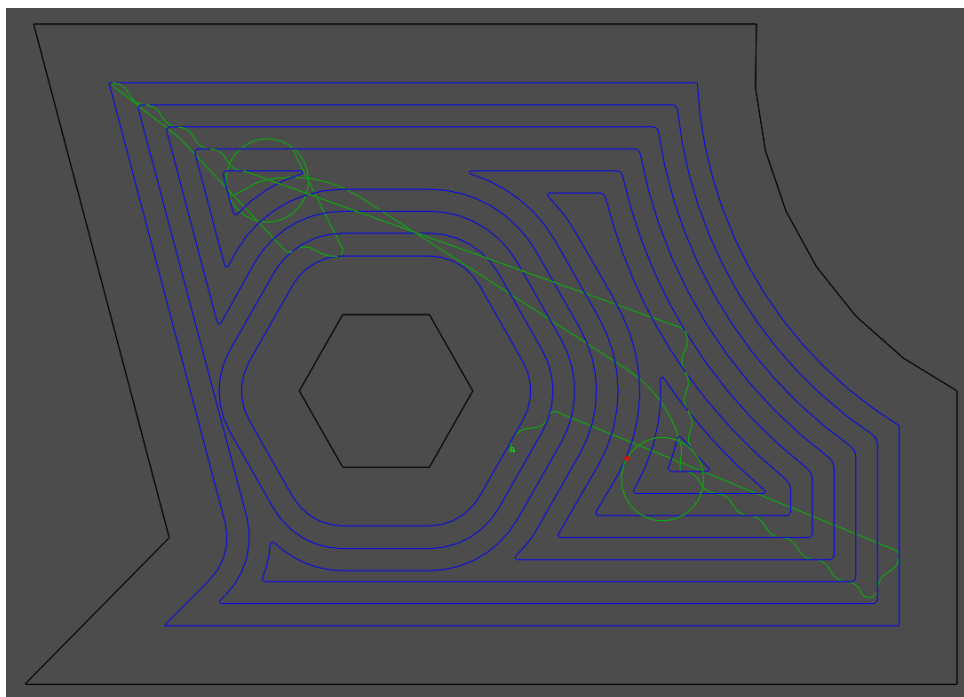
Adaptivní obrábění – detail dráhy druhého modelu
